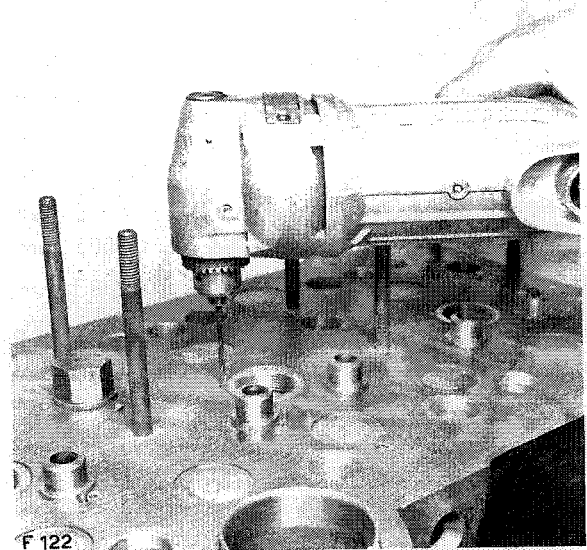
Aufbohren des Sicherungsstifts der Ringmutter zur Befestigung der Düsenführungshülsen
